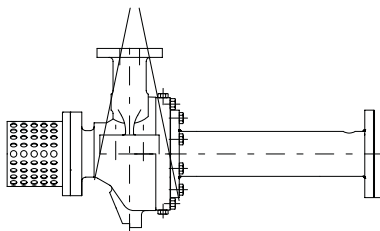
Транспортировка корпуса насоса и части промежуточной подвески
